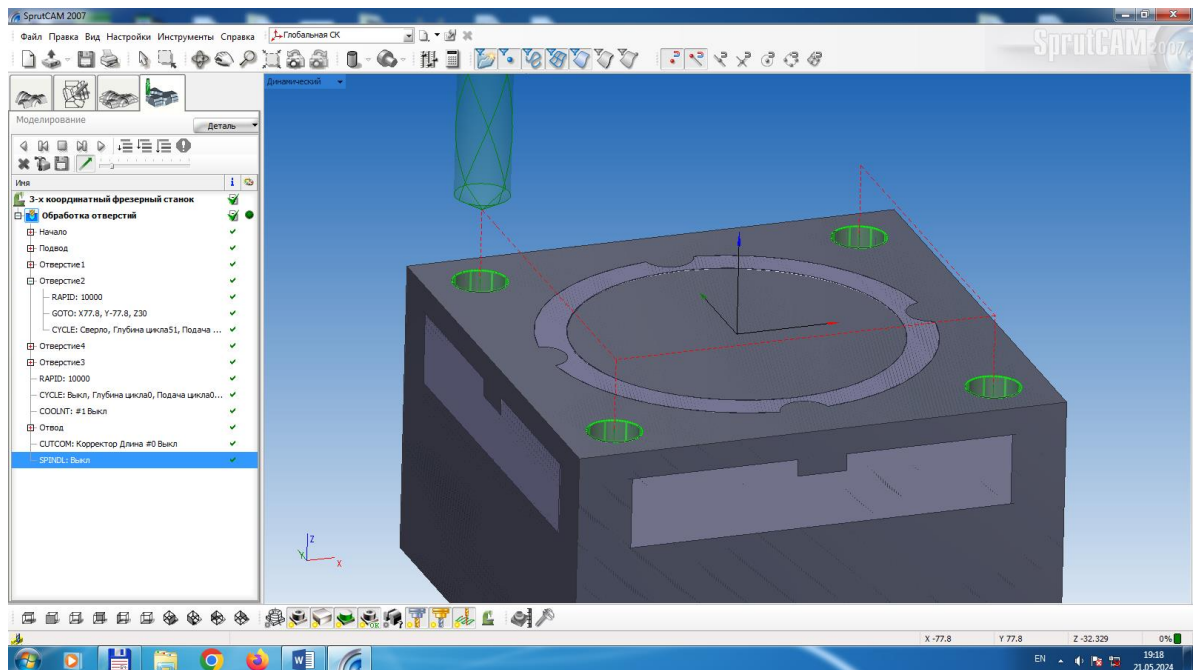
Інструмент перед свердлінням і траєкторія руху свердла
